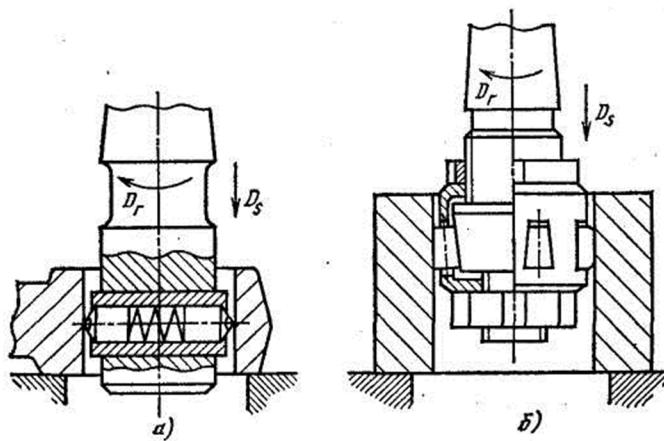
Схемы обработки отверстий выглаживанием и накатыванием
